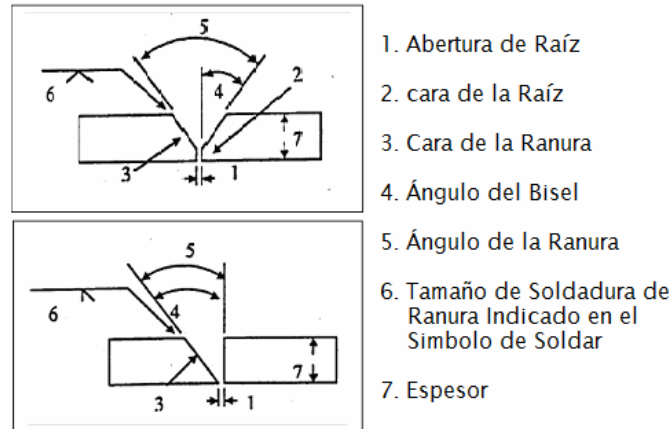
Especificación de geometría en unión soldada para construcción de línea de piping
